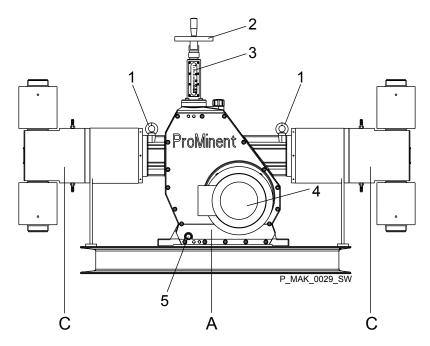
Vista do lado do motor (aqui M5Ka D)
